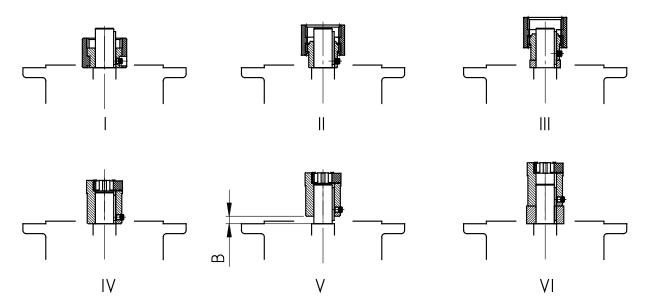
Установка муфты на вал двигателя при различных конструкциях муфты
